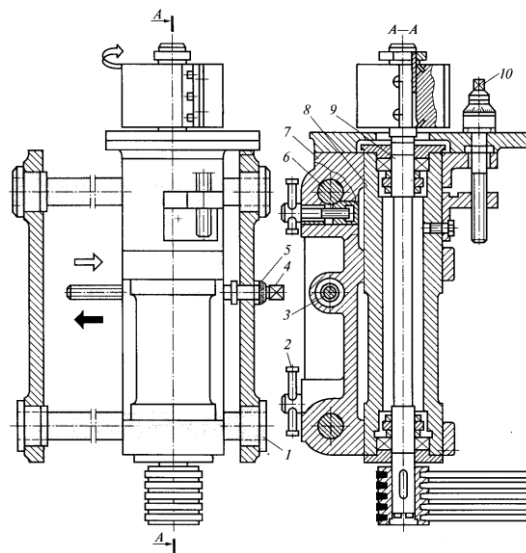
Супорт з круглими напрямними: 1 – ексцентрикова втулка; 2 – рукоятка затискача каретки; 3 – гайка; 4 – гвинт горизонтального настроювання; 5 – лімба; 6 – качалка; 7 – каретка; 8 – гільза; 9 – шпиндель; 10 – гвинт вертикального настроювання
